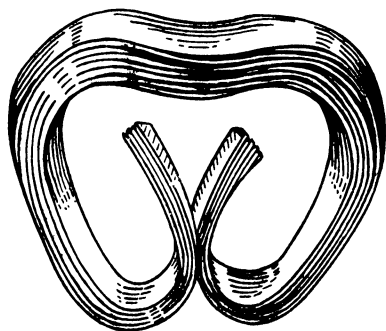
Пакет двухвитковых элементов для поэлементной шихтовки разъемного ленточного сердечника.
